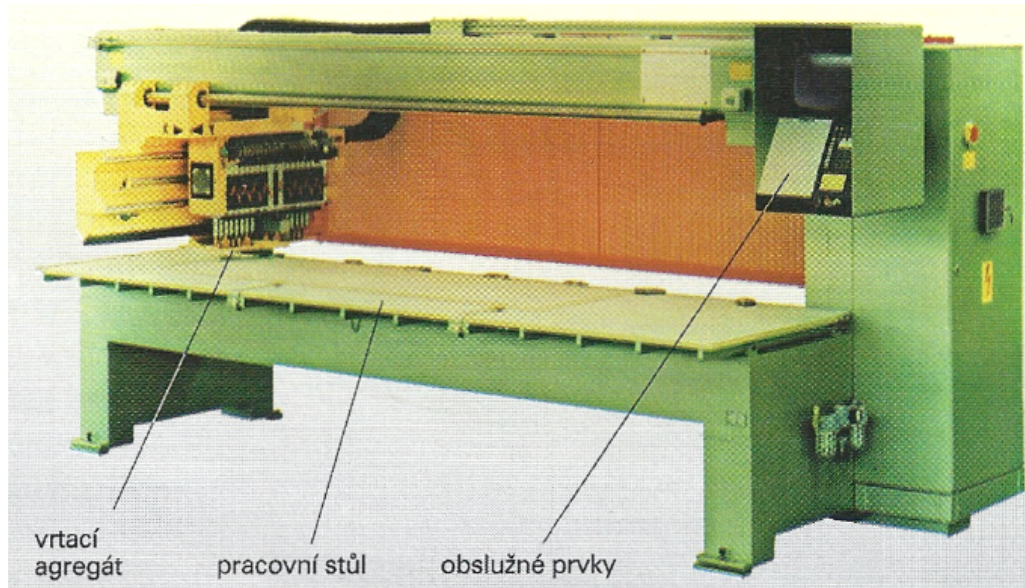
CNC horní frézka s měničem nástrojů (NUTSCH, W.)
